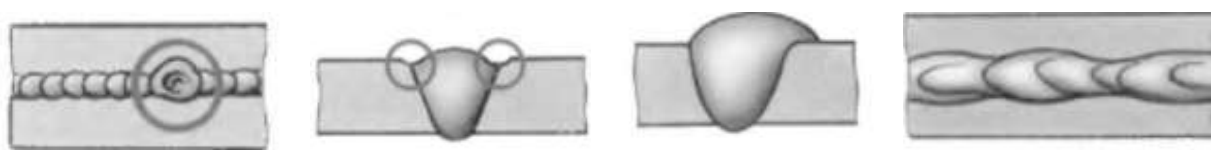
Дефекти зварних з'єднань
